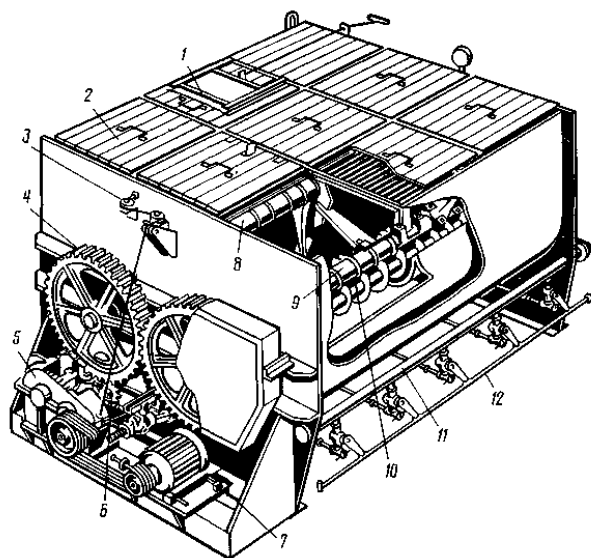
Запарник-смеситель кормов С-12: 1 - крышка смесителя; 2 - щит; 3 - система управления шнеком и задвижкой; 4 - зубчатые колеса; 5 - редуктор привода; 6 - натяжное устройство цепной передачи; 7 - натяжное устройство; 8, 9 - левый и правый лопастные валы; 10 - выгрузной шнек; 11 - парораспределитель; 12 - система управления парораспределителя
